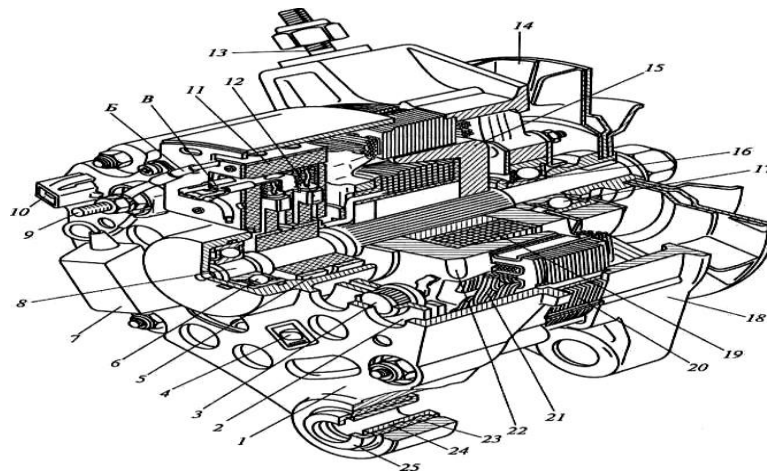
Генератор: 1 – крышка со стороны контактных колец; 2 – выпрямительный блок; 3 – вентиль выпрямительного блока; 4 – винт крепления выпрямительного блока; 5 – контактное кольцо; 6 – задний шарикоподшипник; 7 – конденсатор; 8 – вал ротора; 9 – вывод клеммы «30» генератора; 10 – вывод штекера «61» генератора; 11 – регулятор напряжения; 12 – щетка; 13 – шпилька крепления генератора к натяжной планке; 14 – шкив с вентилятором; 15 – полюсный наконечник ротора; 16 – дистанционная втулка; 17 – передний шарикоподшипник; 18 – крышка привода; 19 – обмотка ротора; 20 – статор; 21 – обмотка статора; 22 – полюсный наконечник ротора; 23 – буферная втулка; 24 – втулка; 25 – поджимная втулка; Б, В – выходы регулятора напряжения
